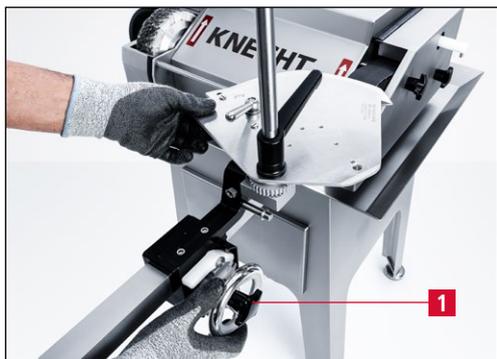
Перемещение приспособления для заточки к шлифовальной ленте
